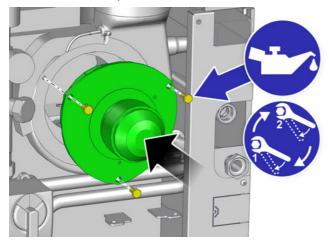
Nettoyage du rotor et remplacement du joint
